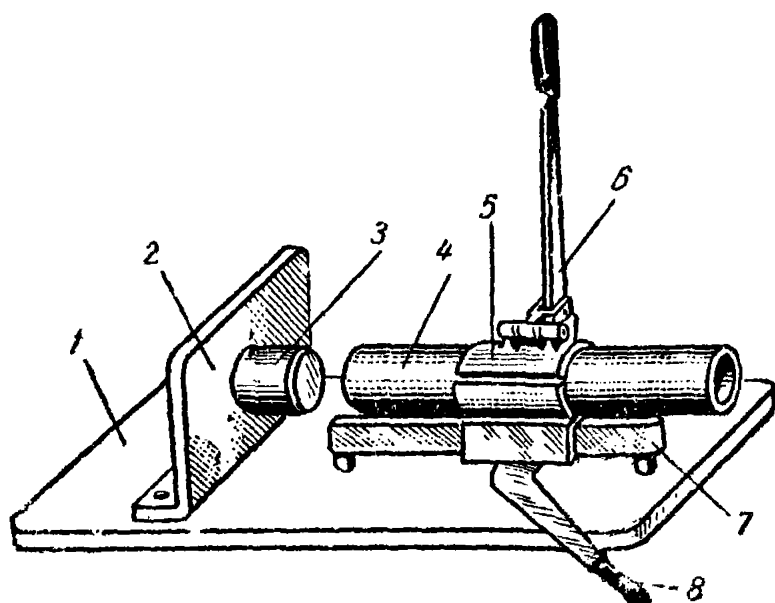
Станок с гладкими оправками для изготовления раструбов неразъемных соединений
